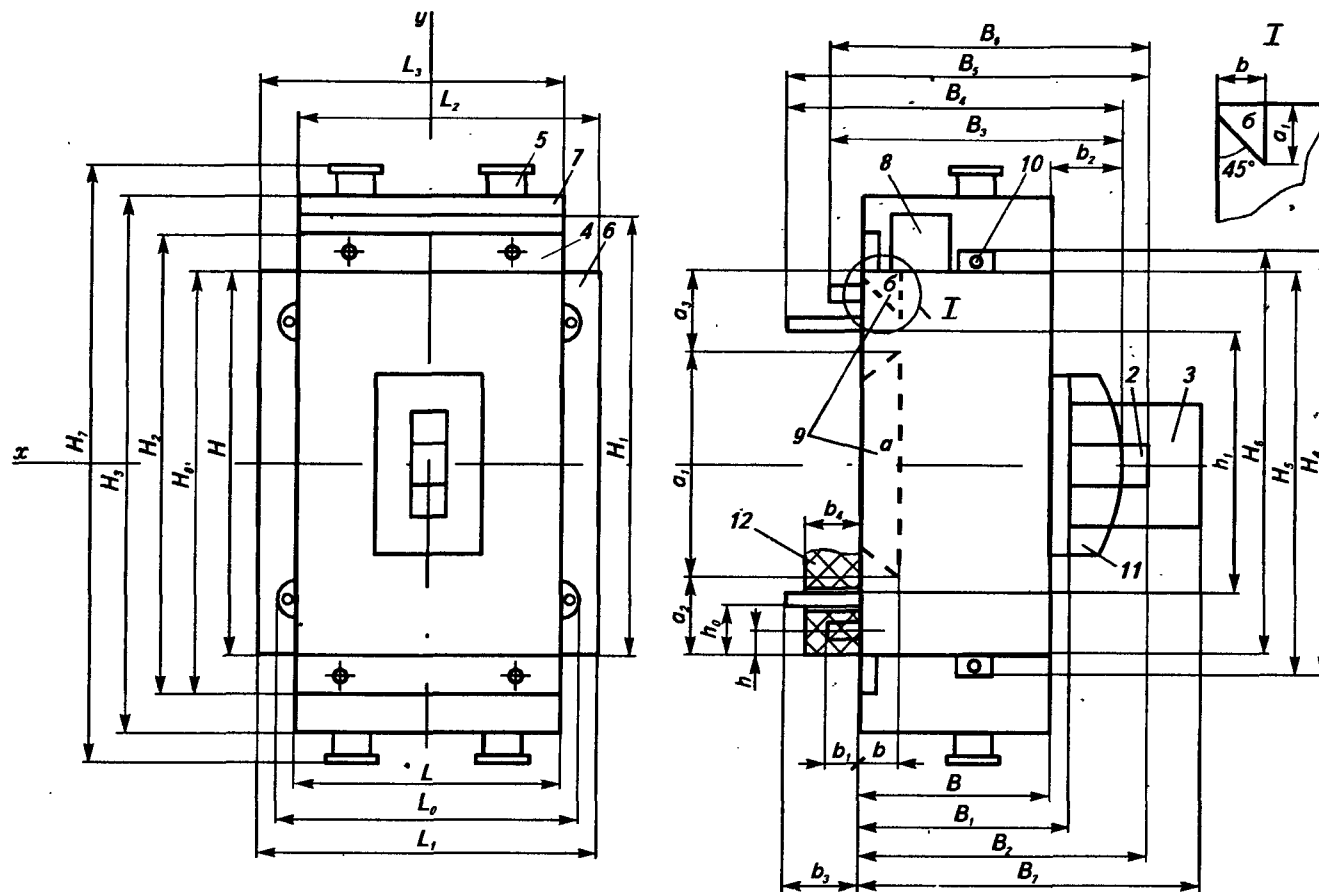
Габаритный чертеж выключателей стационарного исполнения с ручным приводом
